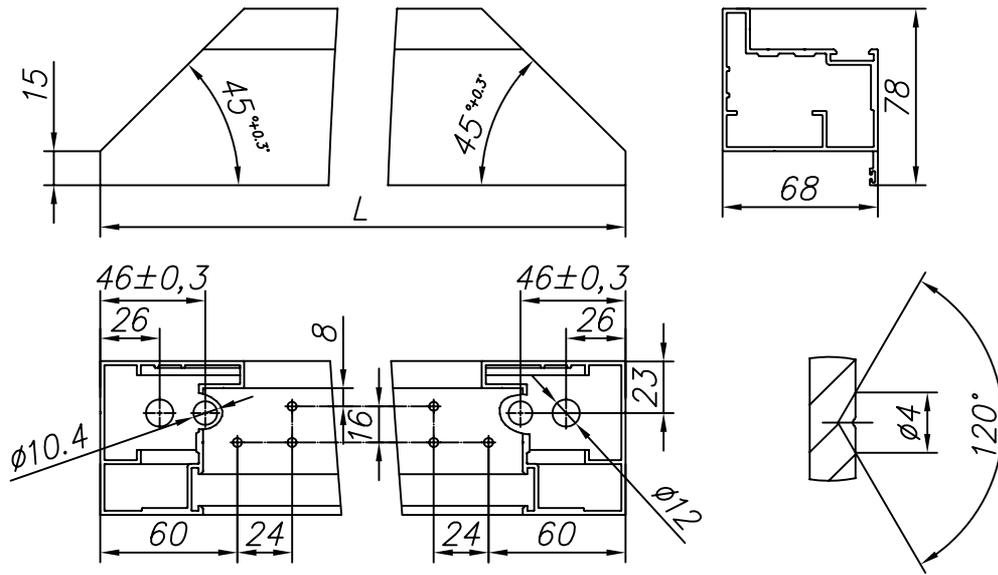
Изготовление стойки без паза для замка из профиля FLGU.400.0110 (открытие внутрь)
